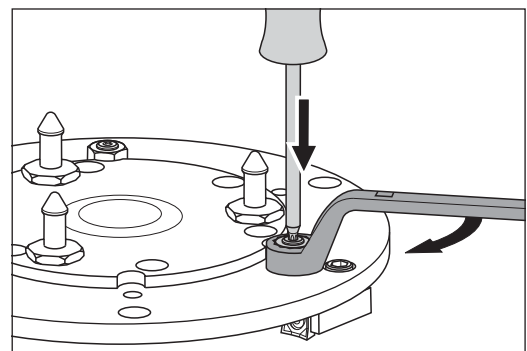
Die Einstellschraube mit dem TORX-Schraubendreher festhalten und gleichzeitig die Mutter im Uhrzeigersinn festziehen.
